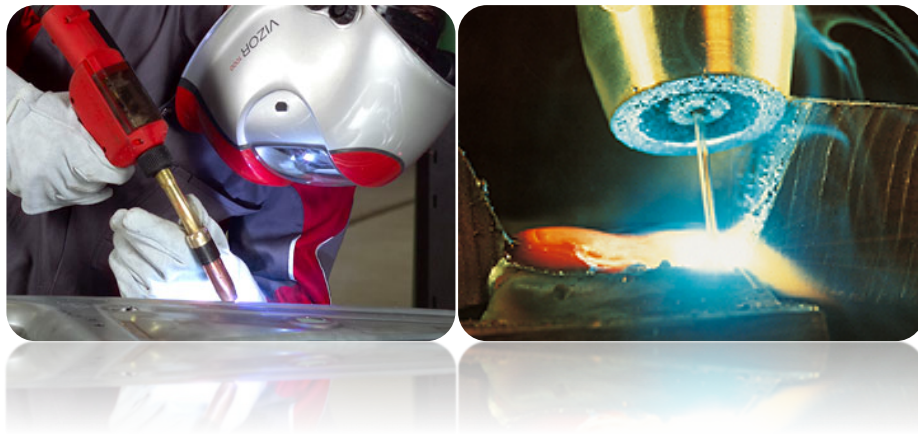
Tècnica de soldadura MIG/MAG.
